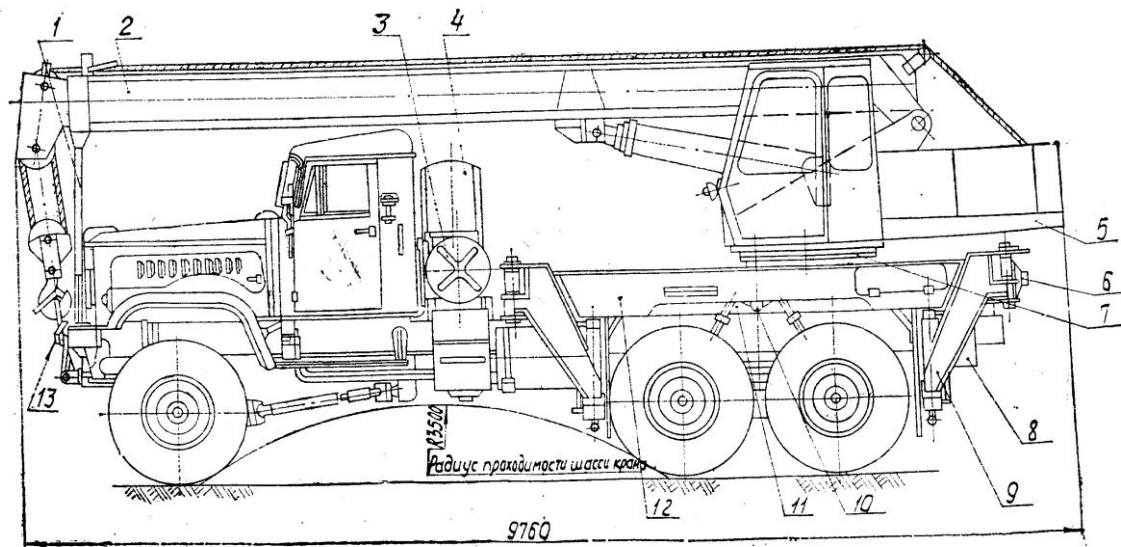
Общий вид крана КС-3572: 1 – стойка; 2 – стрела; 3 – масляный бак; 4 – запасное колесо; 5 – поворотная платформа; 6 – подпятник; 7 – поворотная платформа; 8 – шасси; 9 – выносные опоры; 13 – чалка
